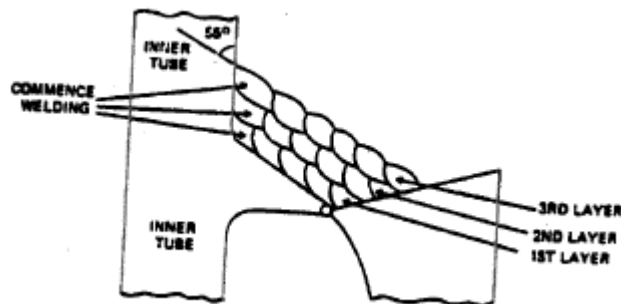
Soudure en corniche - couches déposées à 55° de l'axe des tubes [16].
